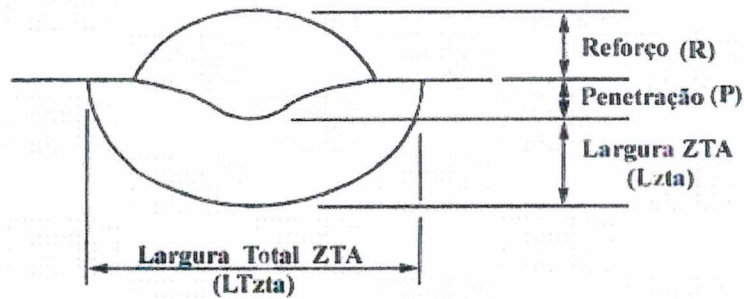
Representação das dimensões características do cordão de solda e da ZTA.
